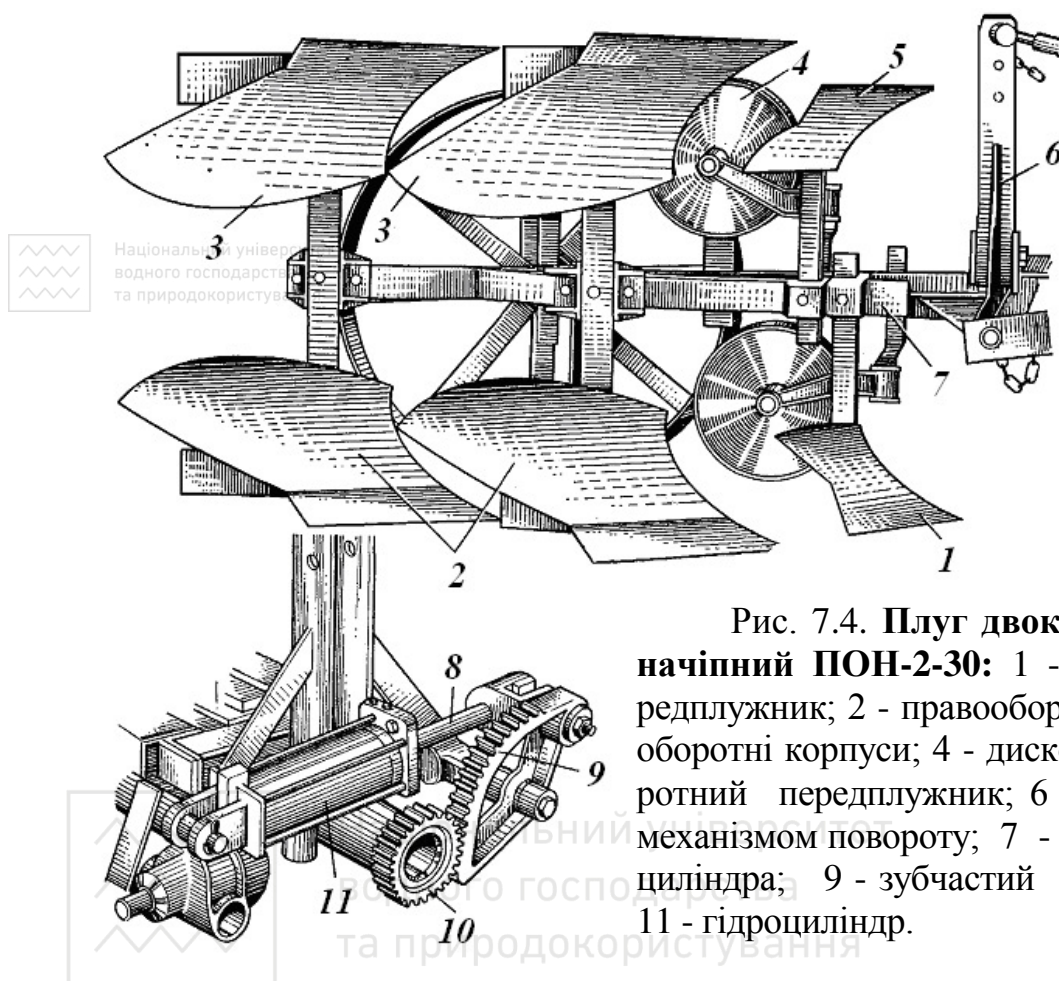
Плуг двокорпусний оборотний начіпний ПОН-2-30: 1 - правооборотний передплужник; 2 - правооборотні корпуси; 3 - лівооборотні корпуси; 4 - дисковий ніж; 5 - лівооборотний передплужник; 6 - начіпний пристрій з механізмом повороту; 7 - рама; 8 - шток гідроциліндра; 9 - зубчастий сектор; 10 - шестерня; 11 - гідроциліндр.
